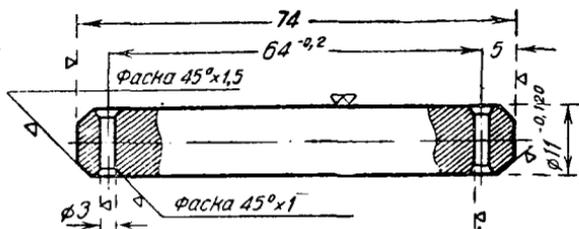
Дет. 433. Палец отжимного рычага муфты сцепления
